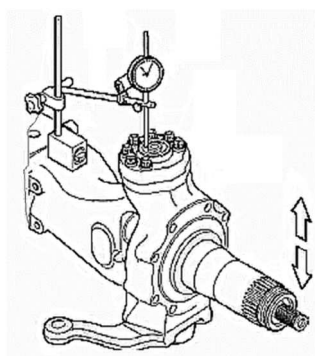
Проверка осевого зазора поворотного кулака
